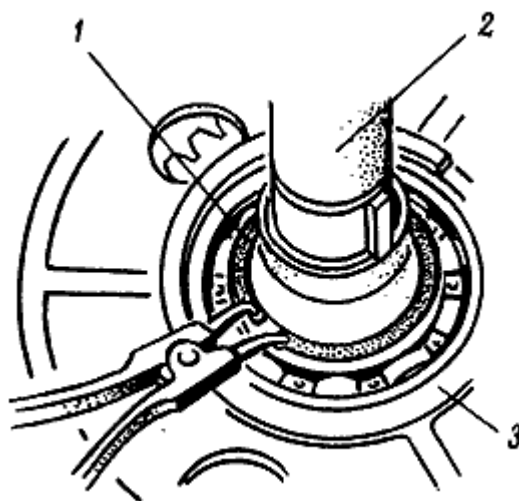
Снятие стопорного кольца подшипника вала сцепления:
